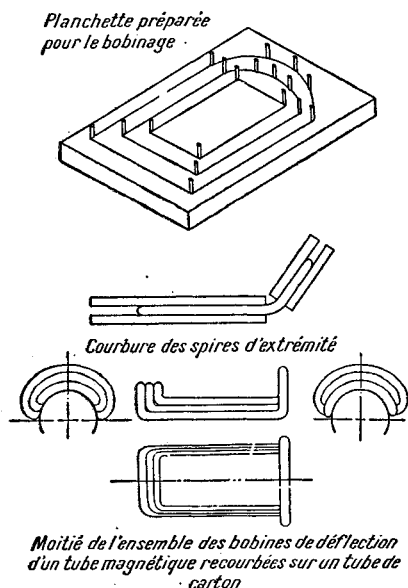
f. — Construction d'un ensemble de bobines de déflexion magnétique.
